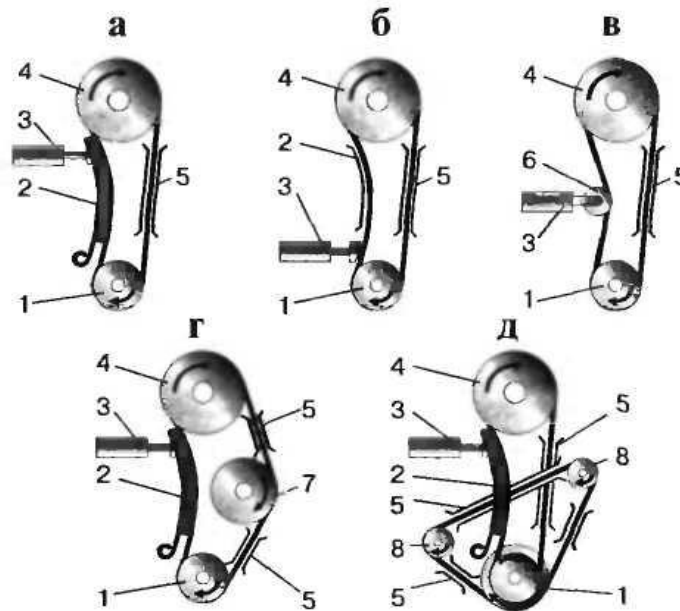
Візуалізація розповсюджених схем використання металевих ланцюгів для обертання газорозподільчого механізму: а – типова схема з профільованим башмаком та автоматичним натяжним пристроєм; б – схема з використанням натяжного пристрою у вигляді ковзного наконечника; в – схема з використанням натяжного пристрою у вигляді обертової зірочки; г – типова схема з додатковим приводом проміжного (паразитного) валу; д – типова схема з застосуванням окремих ланцюгів для обертання балансирних валів чи масло насосу.
